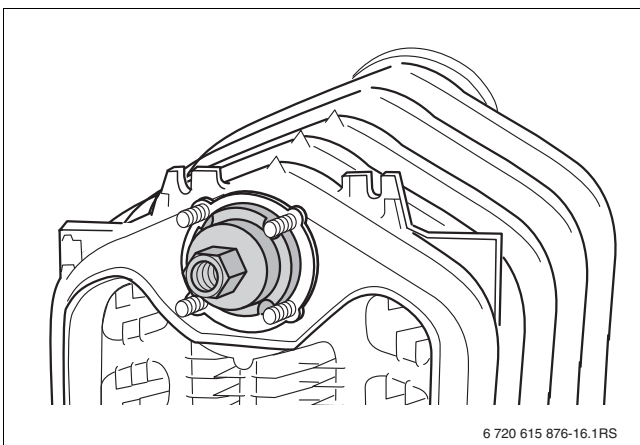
Montaje de las llaves de montaje en el elemento delantero
